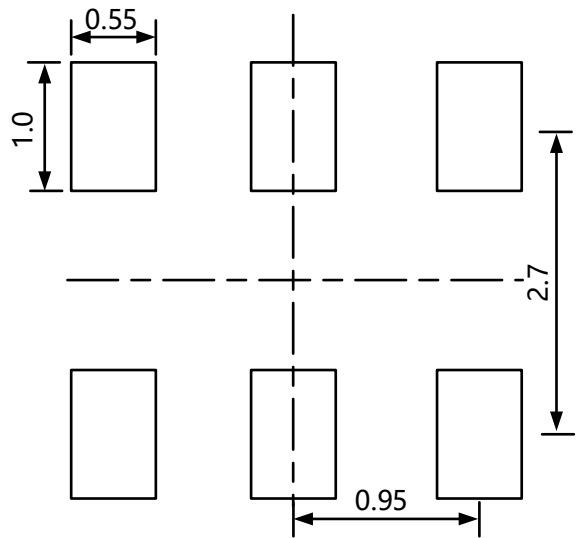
SOT23-6 建议焊盘(所有尺寸单位为 mm)
